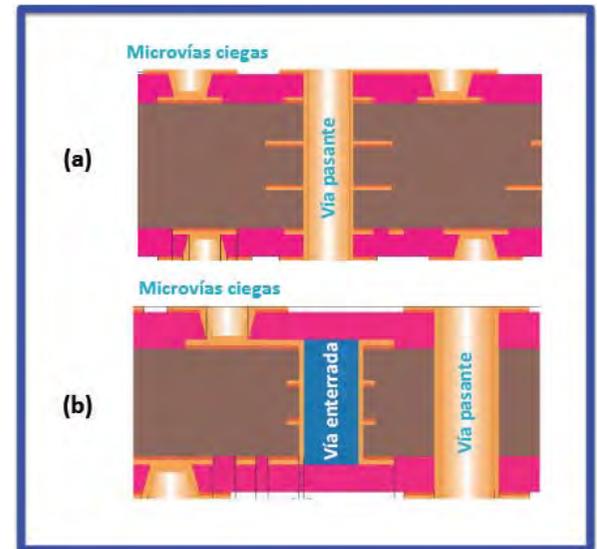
(a) Construcción HDI tipo I. (b) Construcción HDI tipo II
